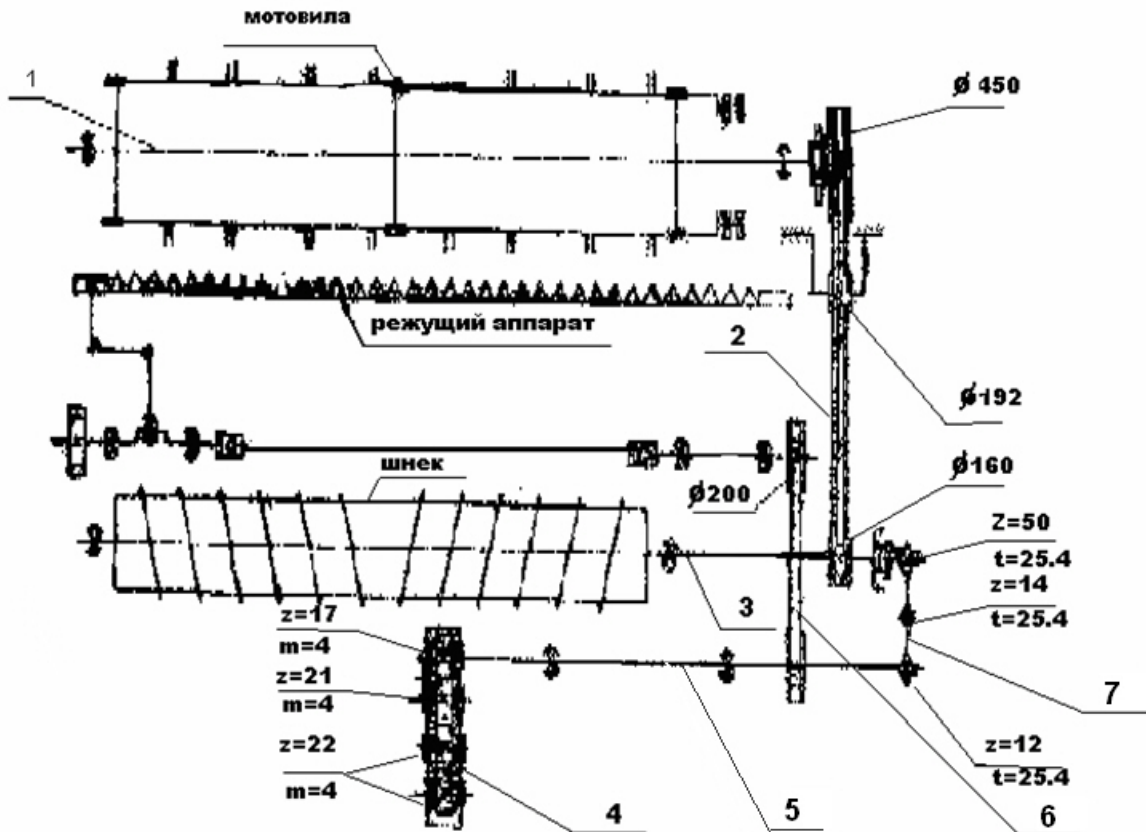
Кинематическая схема жатки для тонко стебельных культур (эксцентриково-шатунный привод с коромыслом режущего аппарата):
